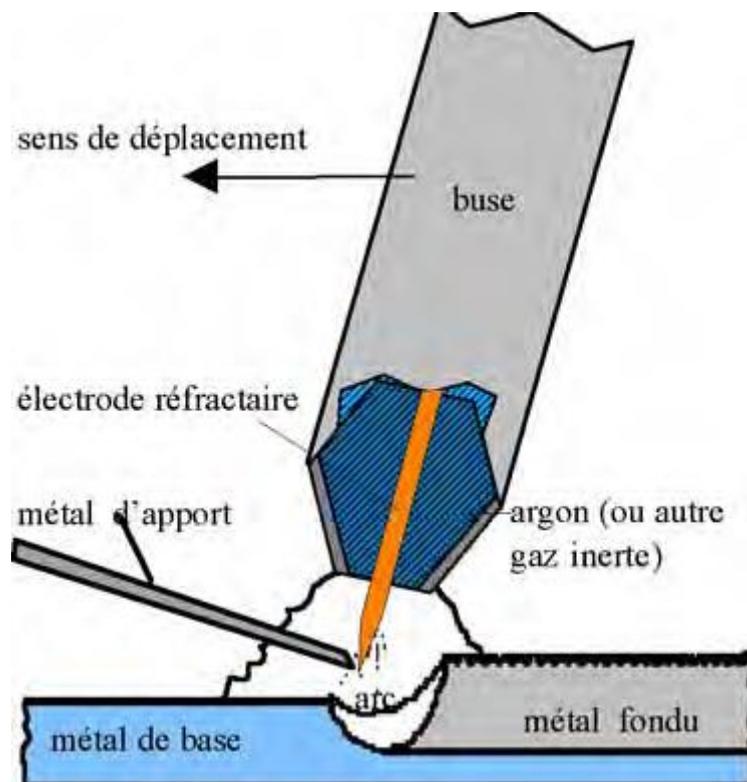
Principe de soudage à l'arc sous protection gazeuse.
